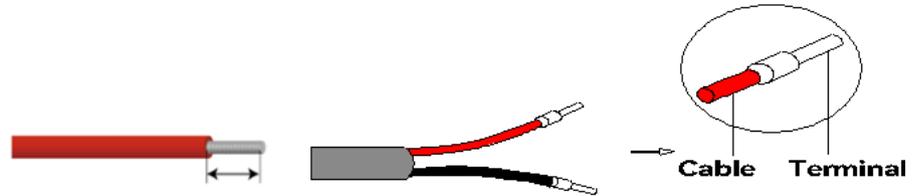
Instalación de los terminales de crimpado aislados en los extremos del cable
